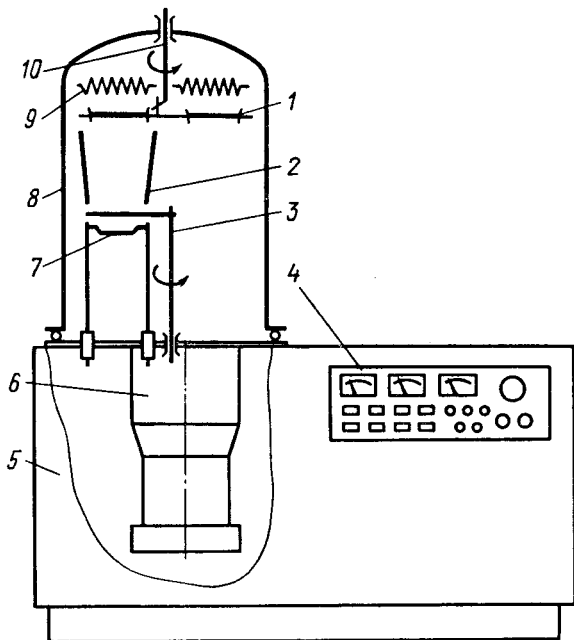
Вакуумная установка с цилиндрической вертикальной рабочей камерой:
